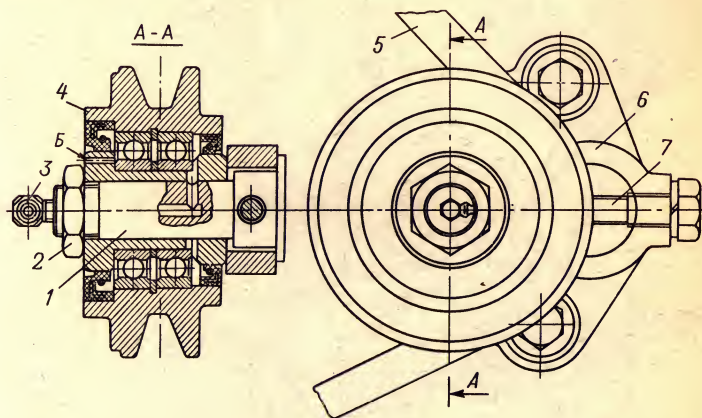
Натяжное устройство ремня вентилятора и водяного насоса двигателей А-41 и А-01М:
